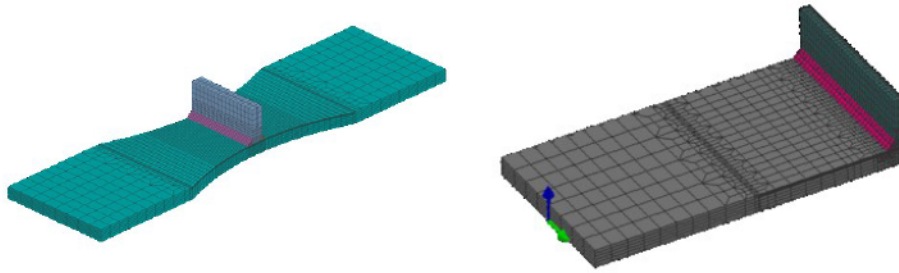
Numerisches Modell einer Probe im Schweißzustand (li.) und einer nach der Reparaturschweißung mit Berücksichtigung der Symmetrie (re.) [Nit15]
